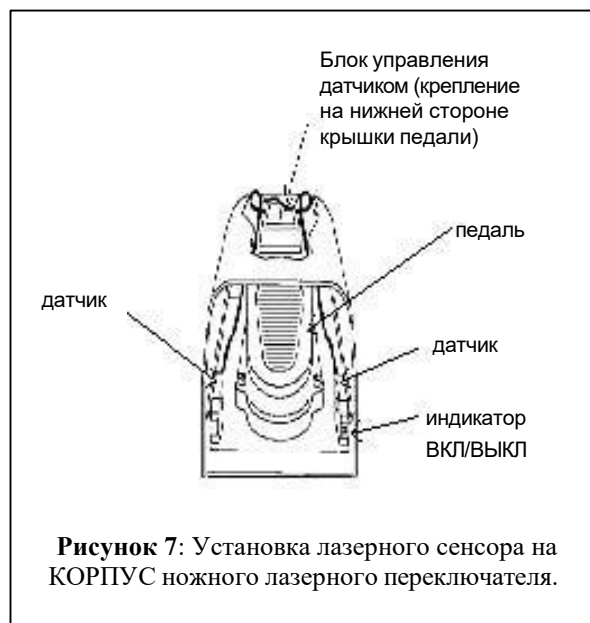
Установка лазерного сенсора на КОРПУС ножного лазерного переключателя.
